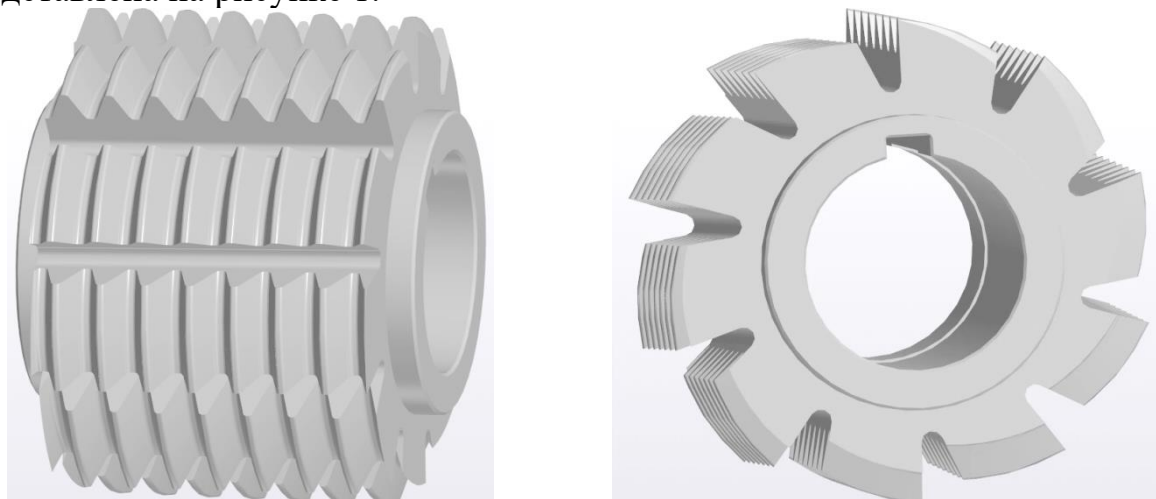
3D модель насадной чистовой червячной зуборезной фрезы
